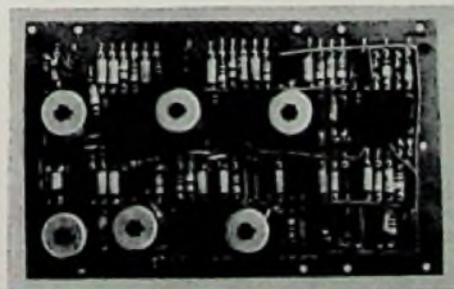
Zf-Verstärker eines PAM-Fernsehempfängers mit gedruckter Schaltung; die gute Übersichtlichkeit der Einzelteile erleichtert die Reparatur (Chassis und Blick auf die Unterseite)
